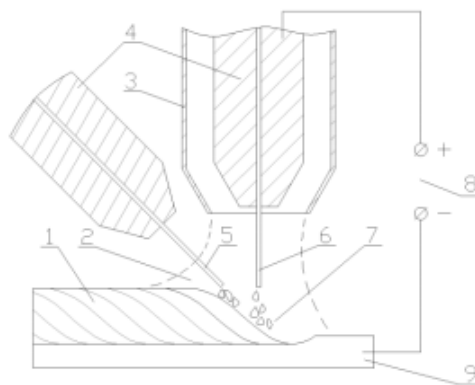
Схема процесса сварки в защитных газах с дополнительной подачей присадочной проволоки
